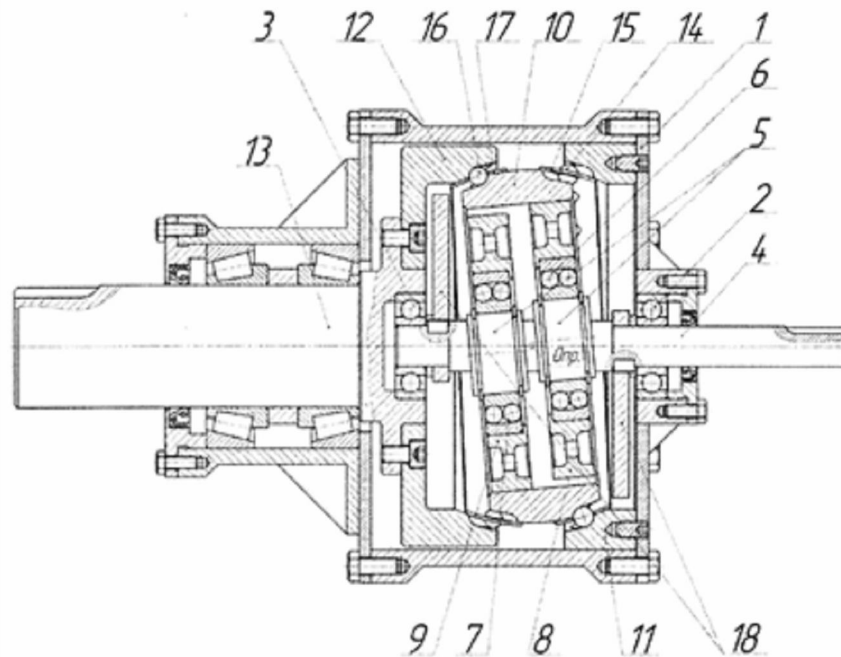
Конструктивная схема ВППТК: 1 – корпус; 2, 3 – подшипники качения; 4 – ведущий вал; 5 – эксцентриковые шейки; 6, 7 – самоустанавливающиеся подшипники качения; 8, 9 – диски; 10 – прецессионное колесо; 11 – неподвижное колесо; 12 – подвижное колесо; 13 – выходной вал; 14, 16 – промежуточные тела качения; 15, 17 – сепараторы; 18 – уравнивающие диски
